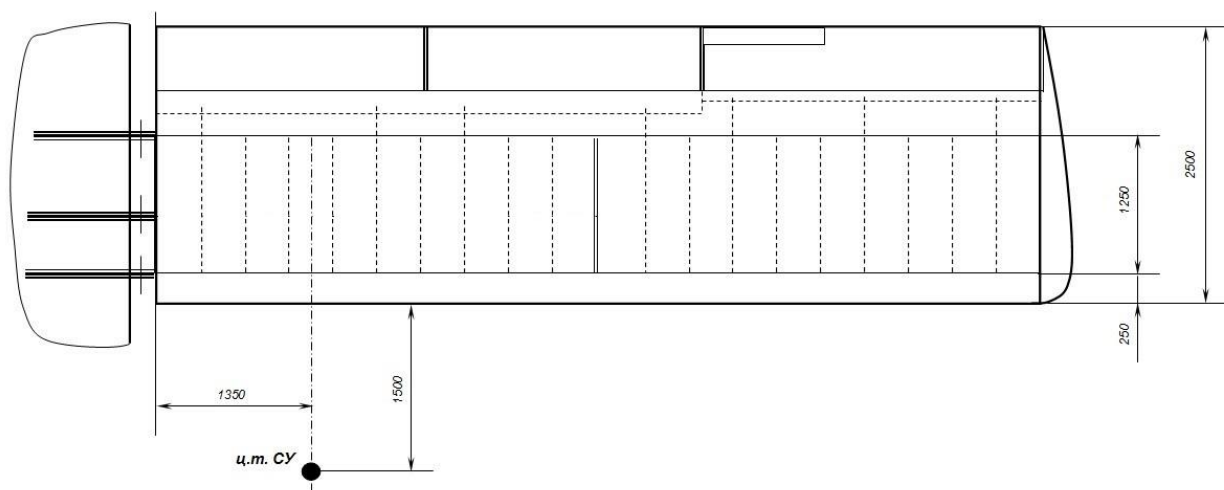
Конструктивно-силова схема крила (вид зверху).
